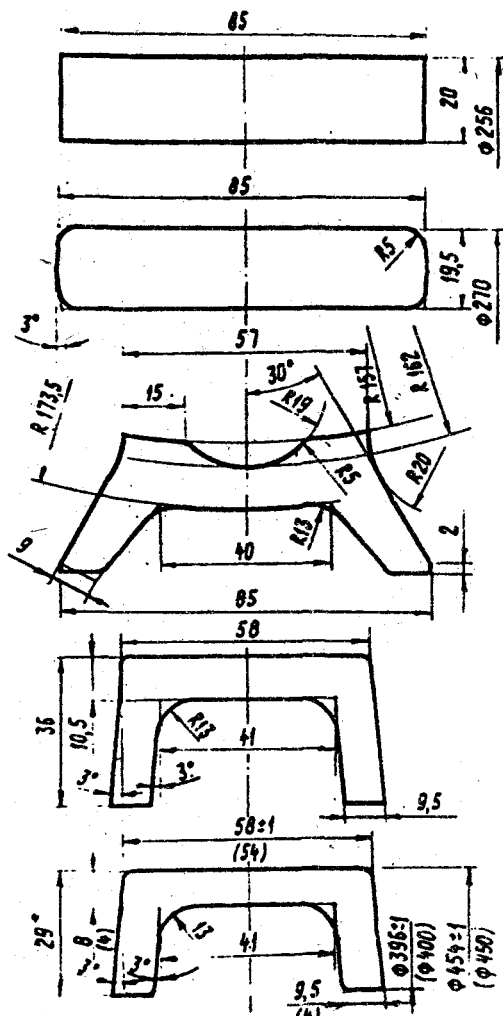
Калибровка заготовки промежуточного кольца дисков из сплава ХН68ВМТЮК-ВД
